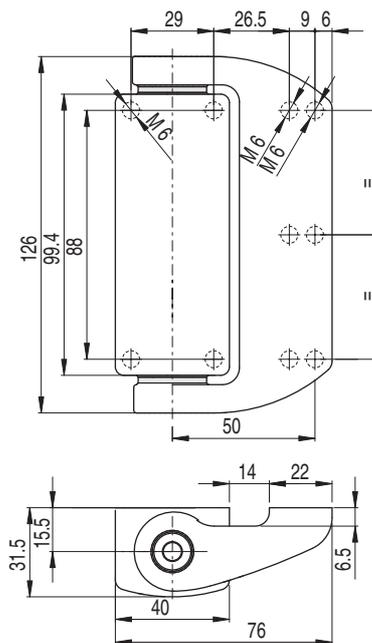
Dimensions de la charnière supplémentaire AC-H-S420 en mm
